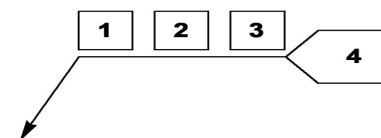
Структура знака условного обозначения сварного соединения по СТБ ISO 2553–2004
